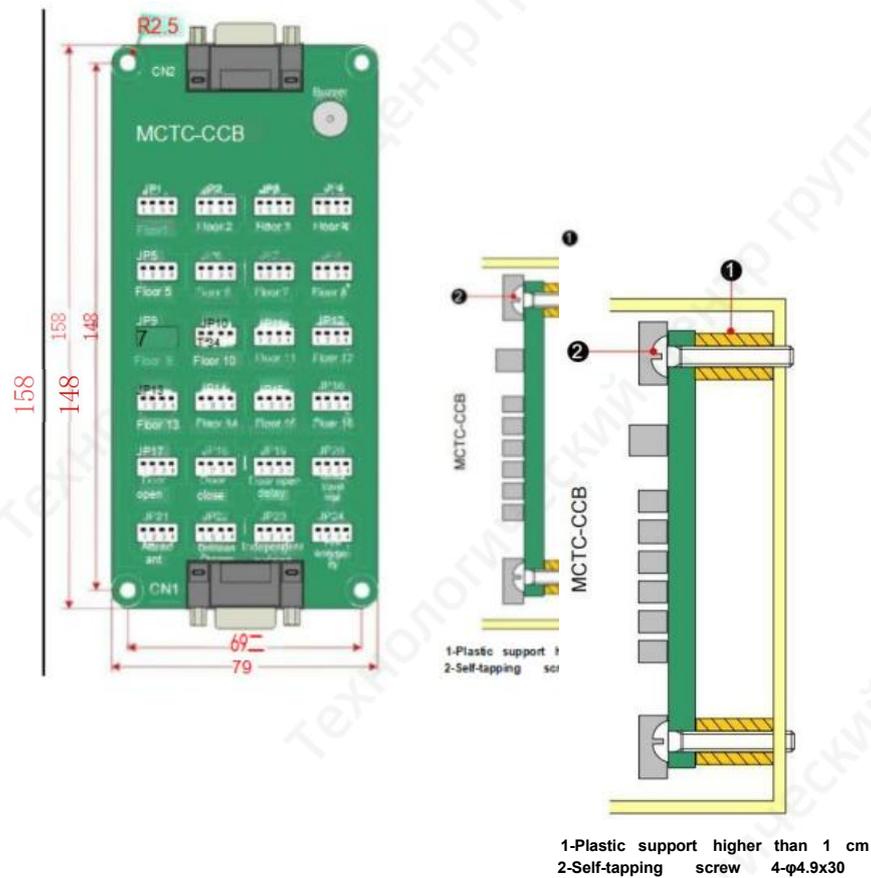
Внешний вид, конструкция и способ установки ЦКБ
